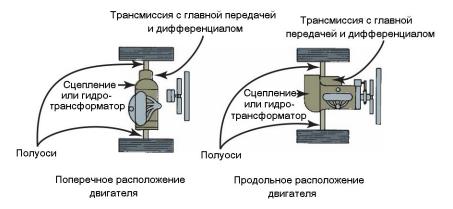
Два типа привода на передние колеса при переднем расположении двигателя: с поперечным расположением (слева) и продольном (справа) расположении двигателя.
